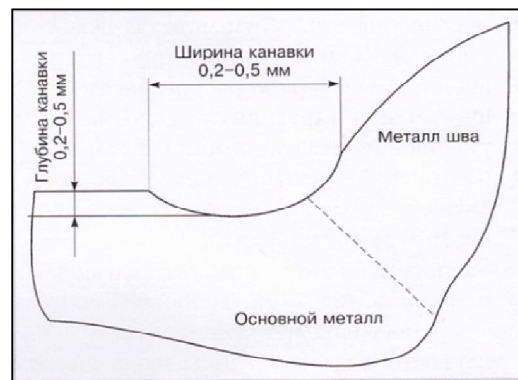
Профиль сварного шва после упрочнения высокочастотной механической проковкой зоны сплавления шва с основным металлом
